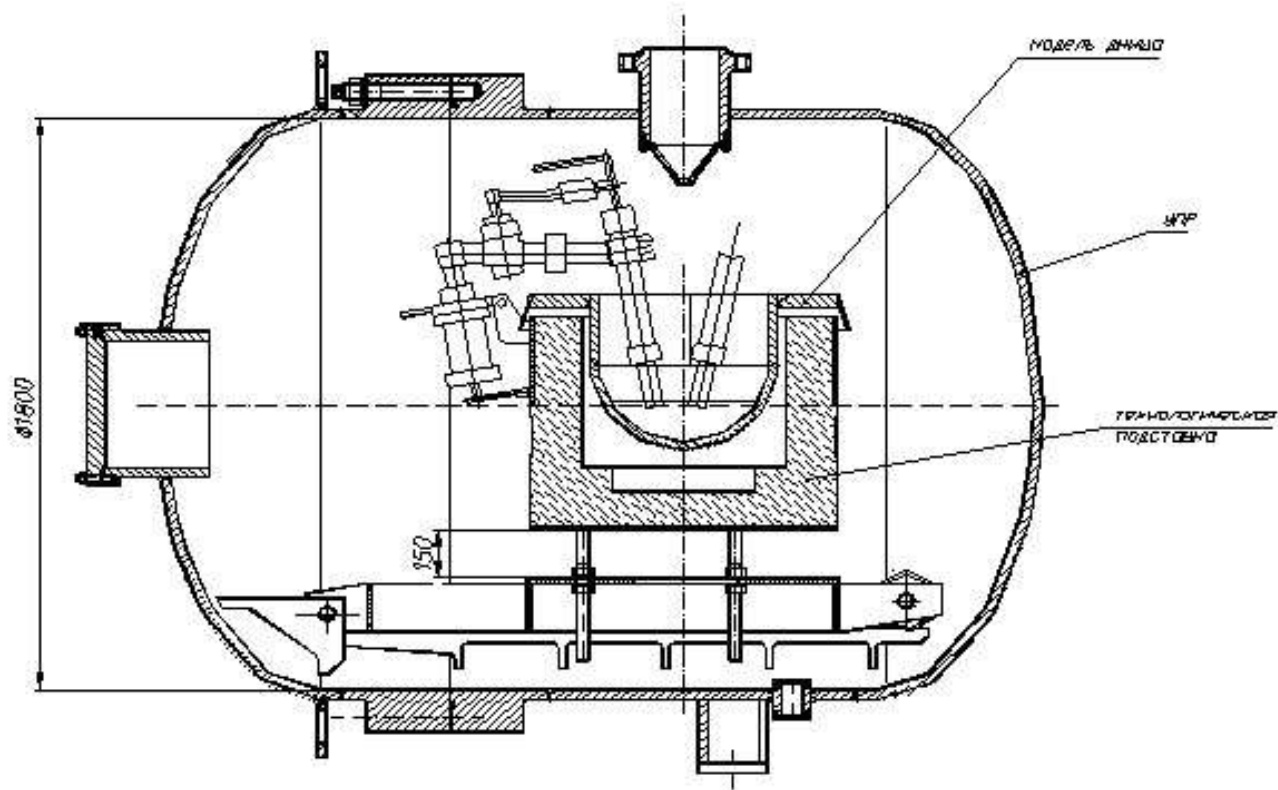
Устройство приема расплава установки ЛАВА-Б
